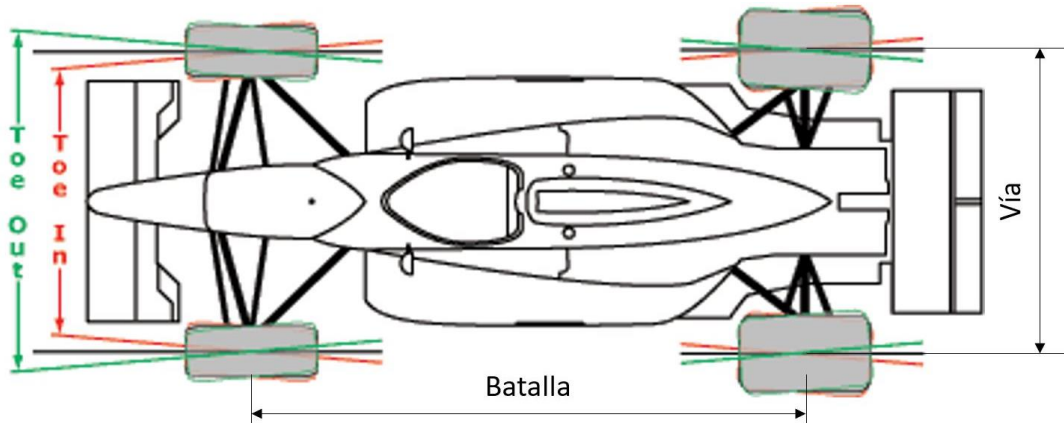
Parámetros en la vista en planta. Fuente: Intrax Racing
